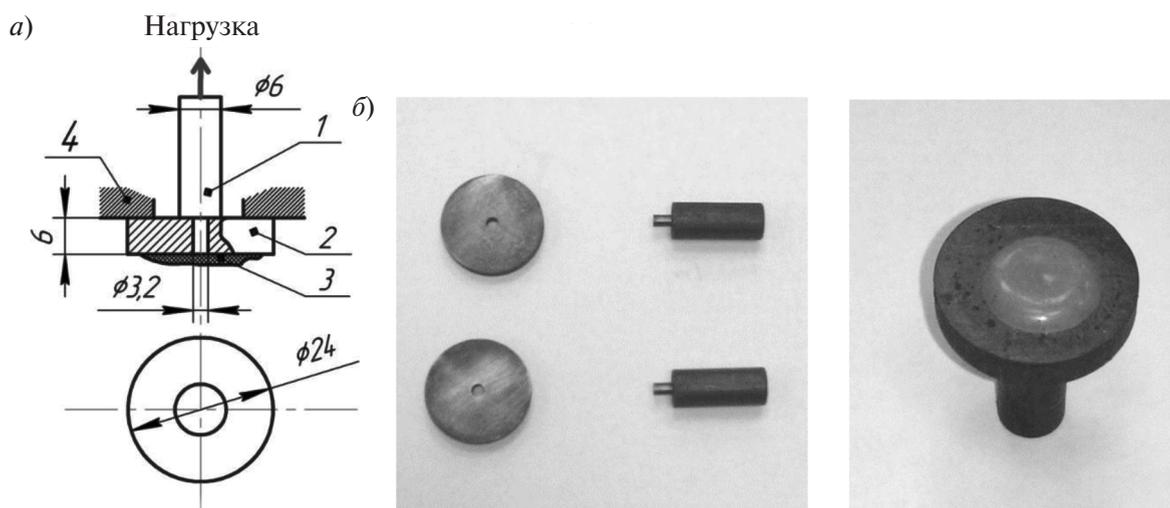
Схема нагружения (а) и общий вид (б) образцов для определения величины адгезии: 1 – стержень; 2 – диск; 3 – полимерное покрытие; 4 – упор
